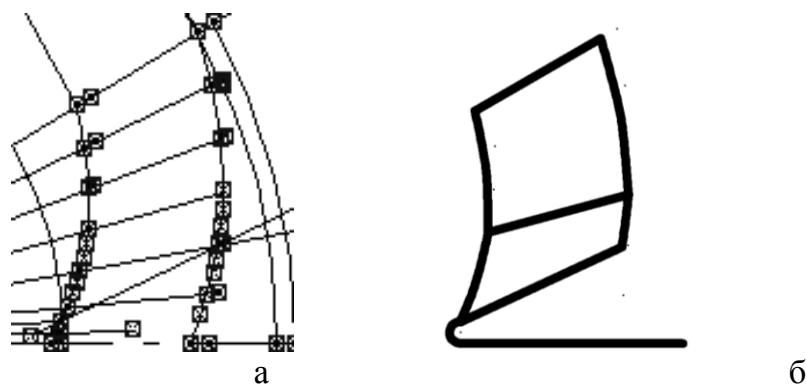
Затилований зуб фрези: а – одноразовий; б - двократний
